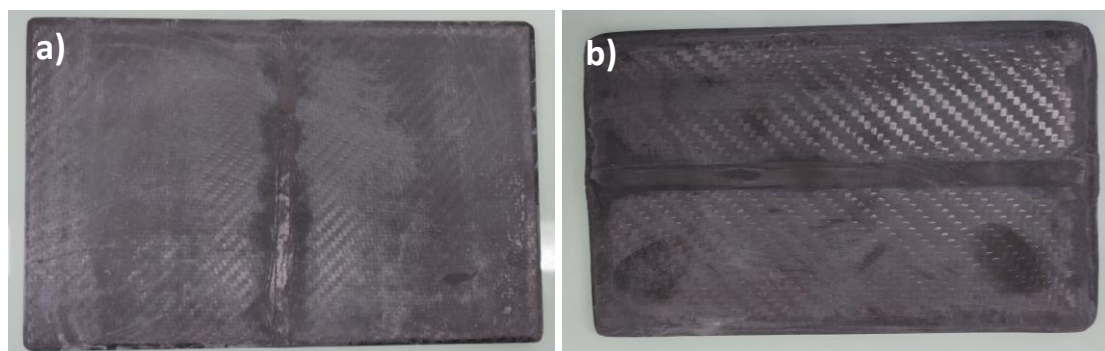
Processo de reparação por preenchimento da fissura: a) placa para provetes para ensaios à tração; b) placa para provetes para ensaios à flexão
